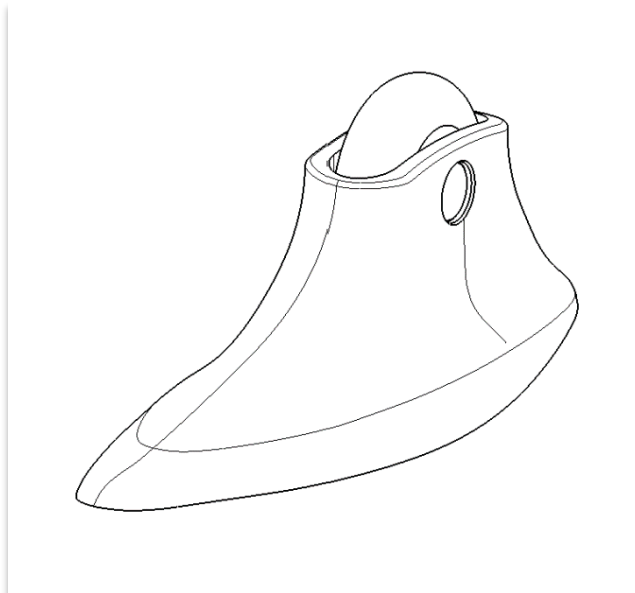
Technische Zeichnung Gesamtansicht Baugruppe montiert
